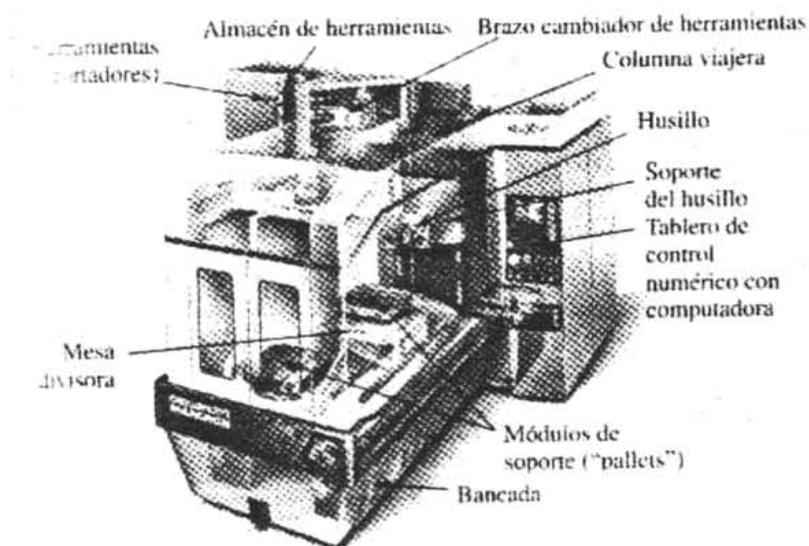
Ilustración de un centro de maquinado con husillo horizontal y cambiador automático de herramientas.
